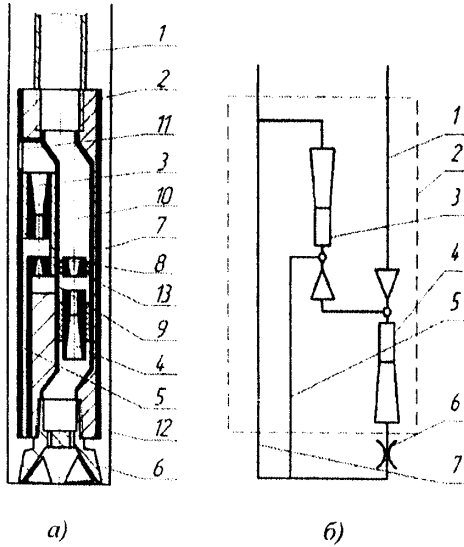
Пристрій для буріння свердловин: а) конструкція; б) гідравлічна схема
